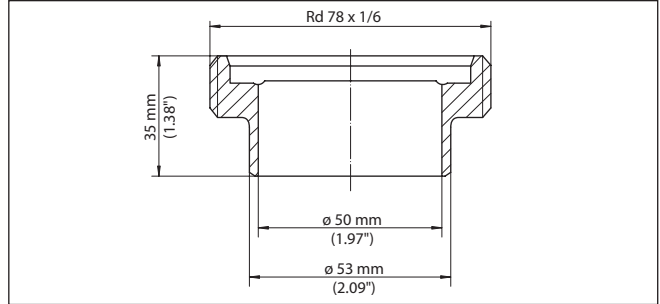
Maße Einschweißstutzen Bundstutzen DN 50 (DIN 11864-1) - VEGABAR 82, 83
